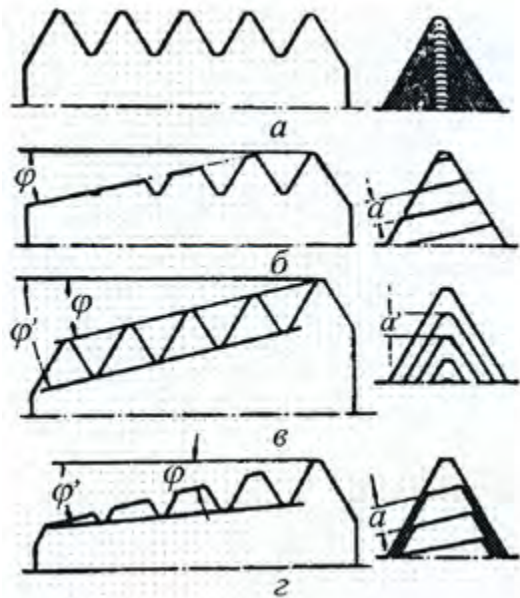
Схеми розташування зубців багатониткових гребінок
